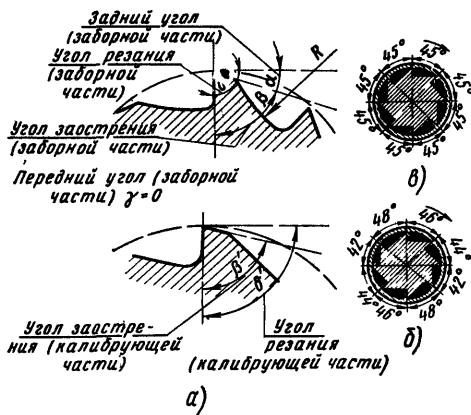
Геометрия зубьев развертки а — элементы режущих зубьев, б — развертка с неравномерным шагом, в — развертка с равномерным шагом
